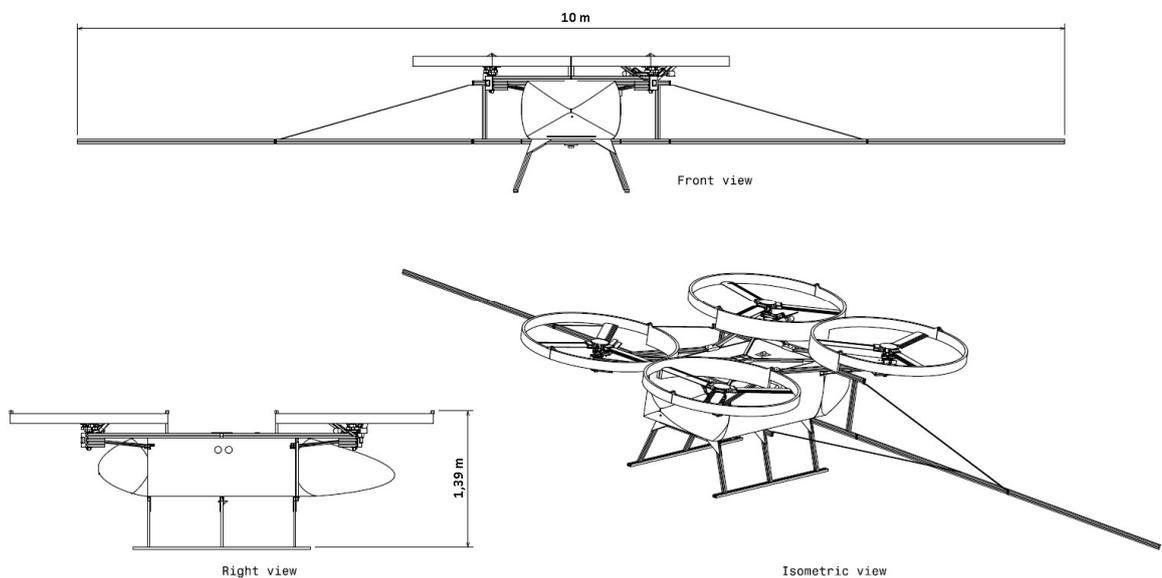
Dimensiones del Drone configuración para pulverizar.
